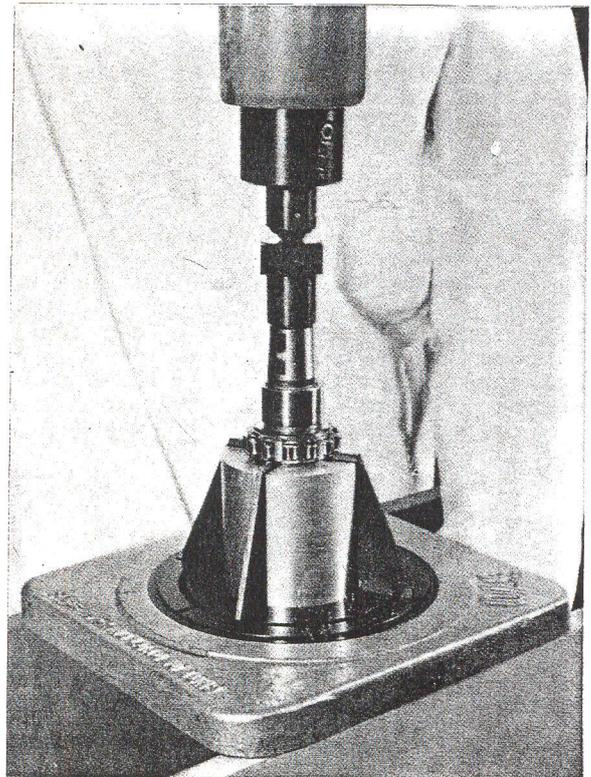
Dépose du roulement et du manchon d'arbre.
